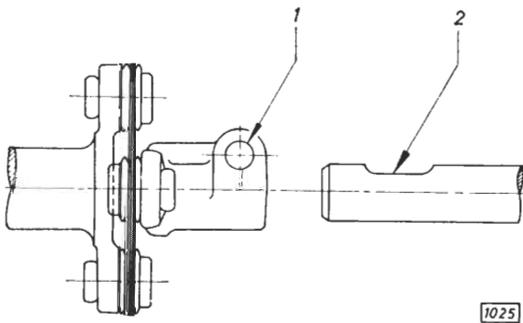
Lage der Lenkspindel zum Lenkspindelflansch
